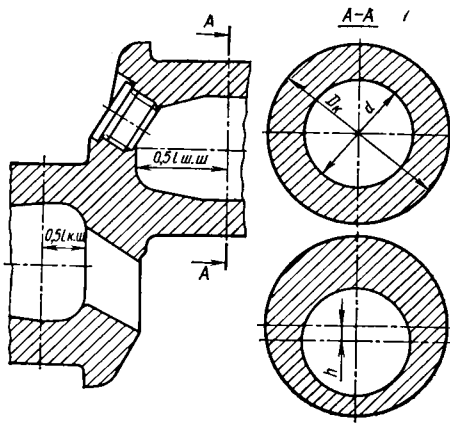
Сечения коренных и шатунных шеек коленчатого вала двигателя
